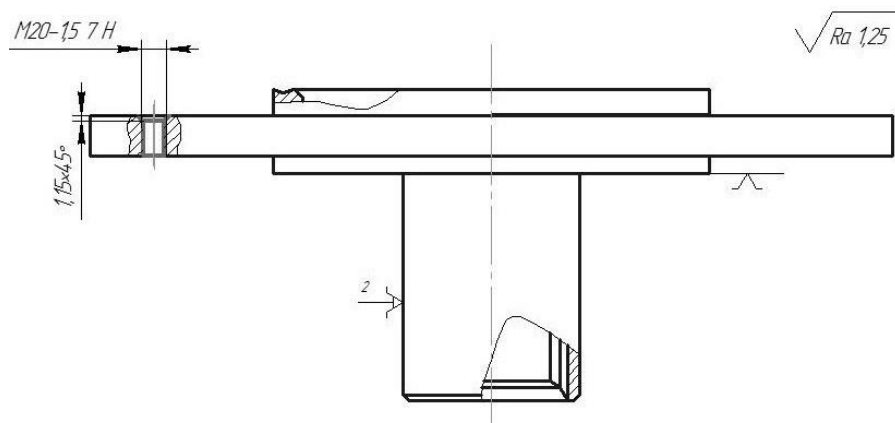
Фланець ведучої частини маточини колеса
